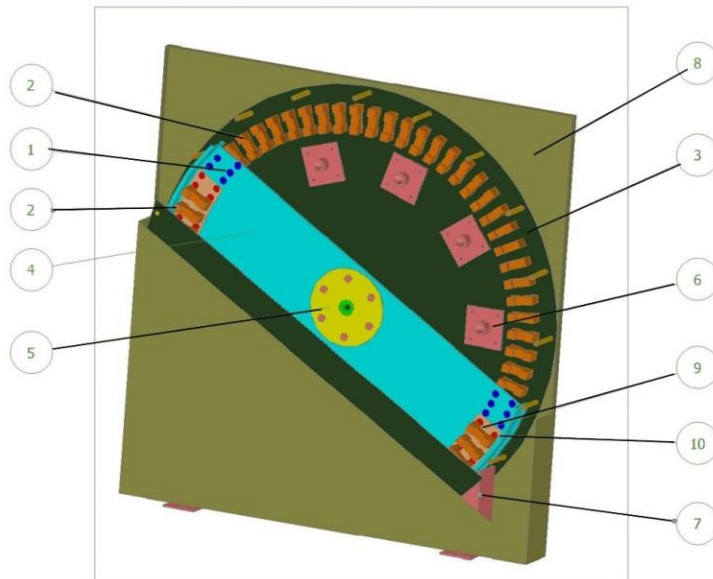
Общий вид двигателя: 1 – постоянные магниты ротора; 2 – электромагниты статора; 3 – корпус статора; 4 – диск с «матрицей»; 5 – подшипниковый узел; 6 – шаровые опоры; 7, 8 – часть корпуса; 9 – прорези дисков; 10 – наконечники из магнитомягкого материала
